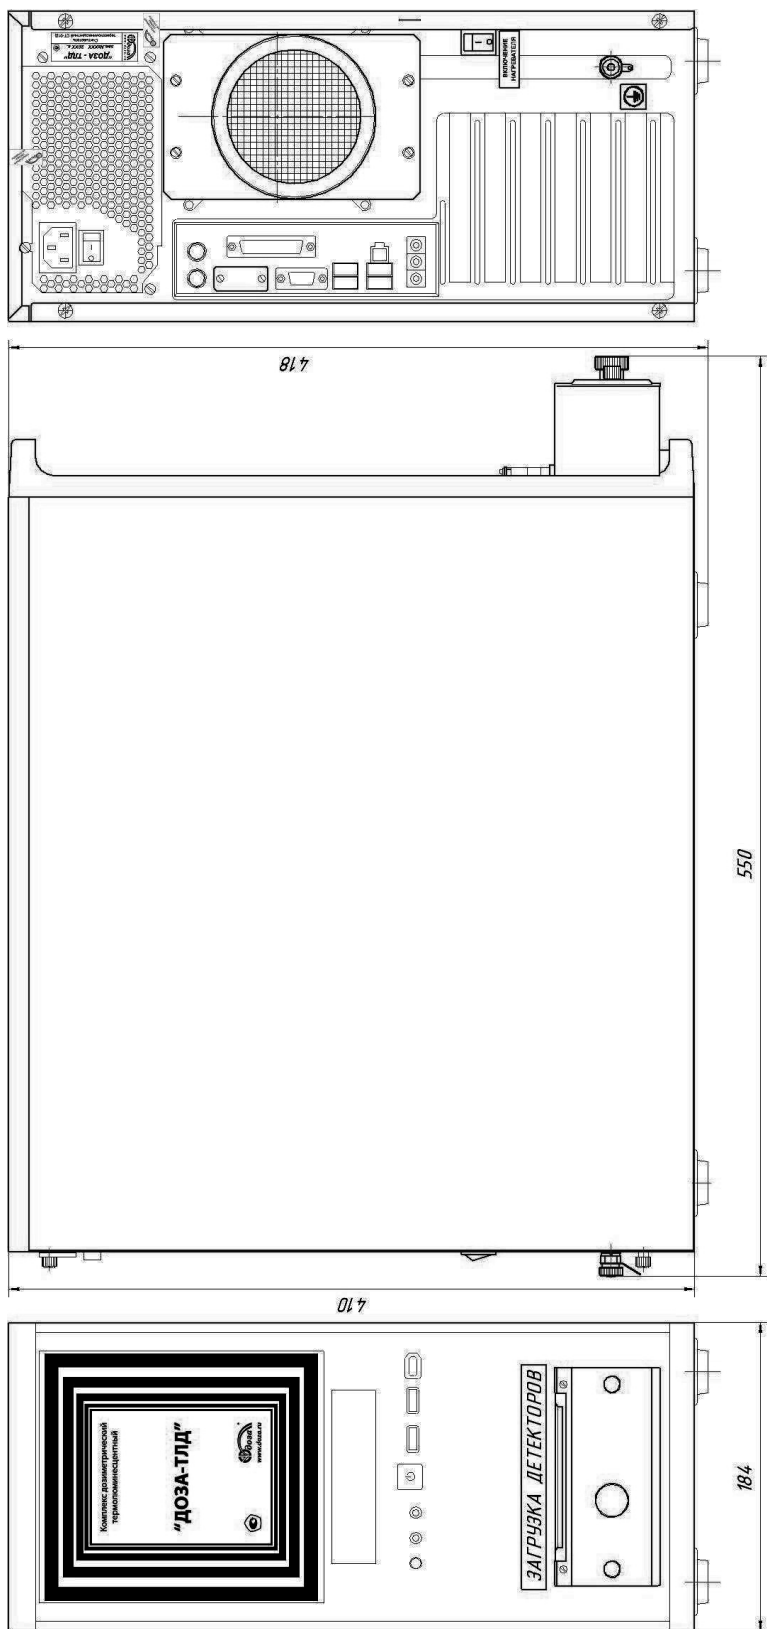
Считыватель термолуминесцентный СТ-01Д ФВКМ.468169.003
